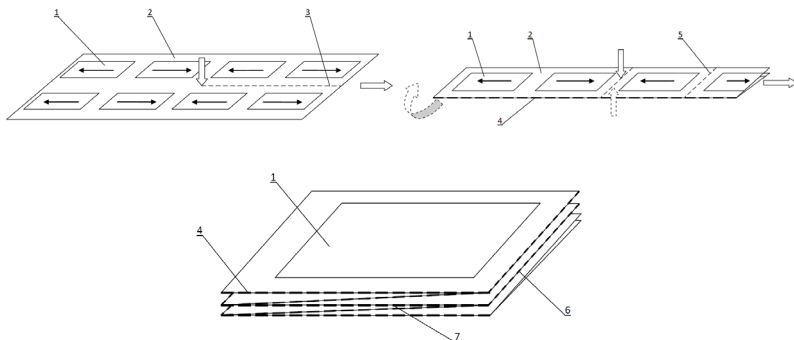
Способ комплектовки книжного блока (одноэлементного)
